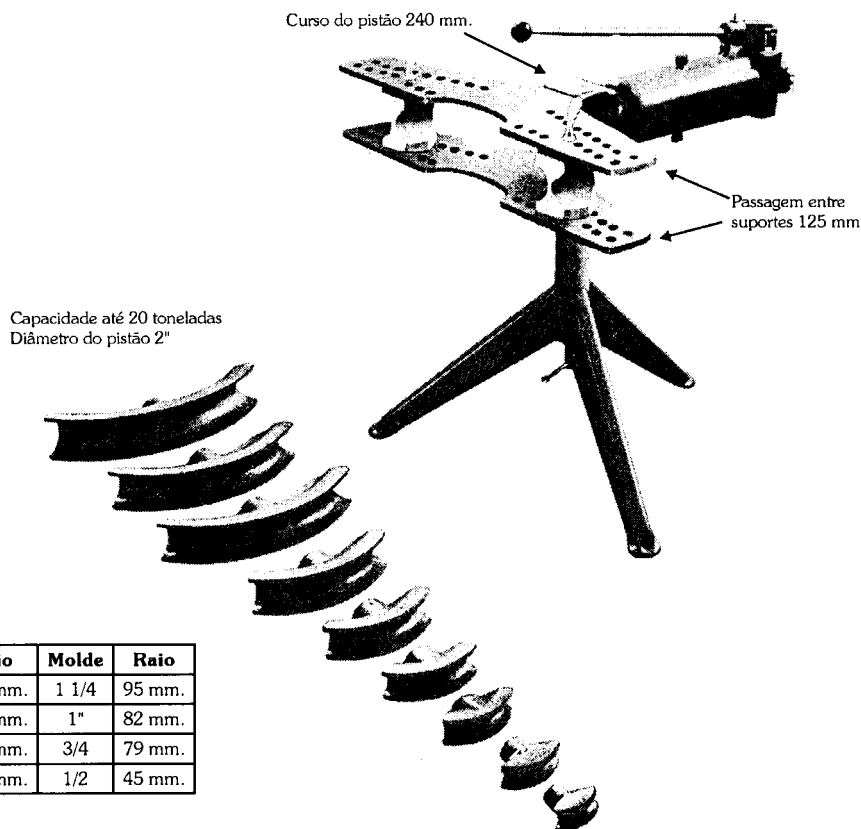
Máquina-ferramenta hidráulica para curvar tubos ou eletrodutos de 1/2" até 3". Cortesia: Marinaro.
